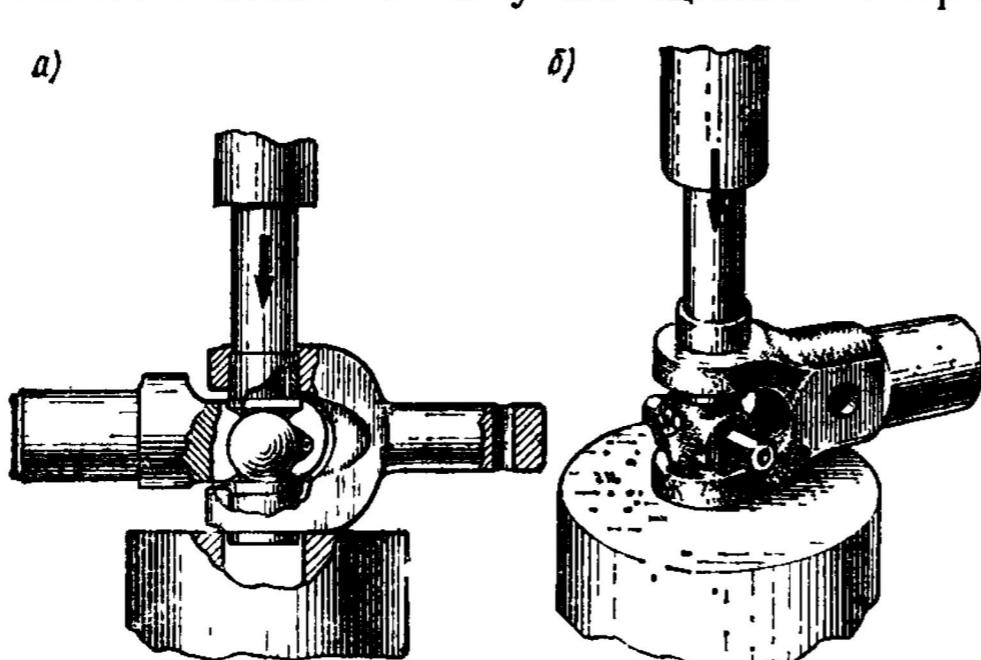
Выпрессовка (а) и запрессовка (б) игольчатого подшипника крестовины карданного шарнира
